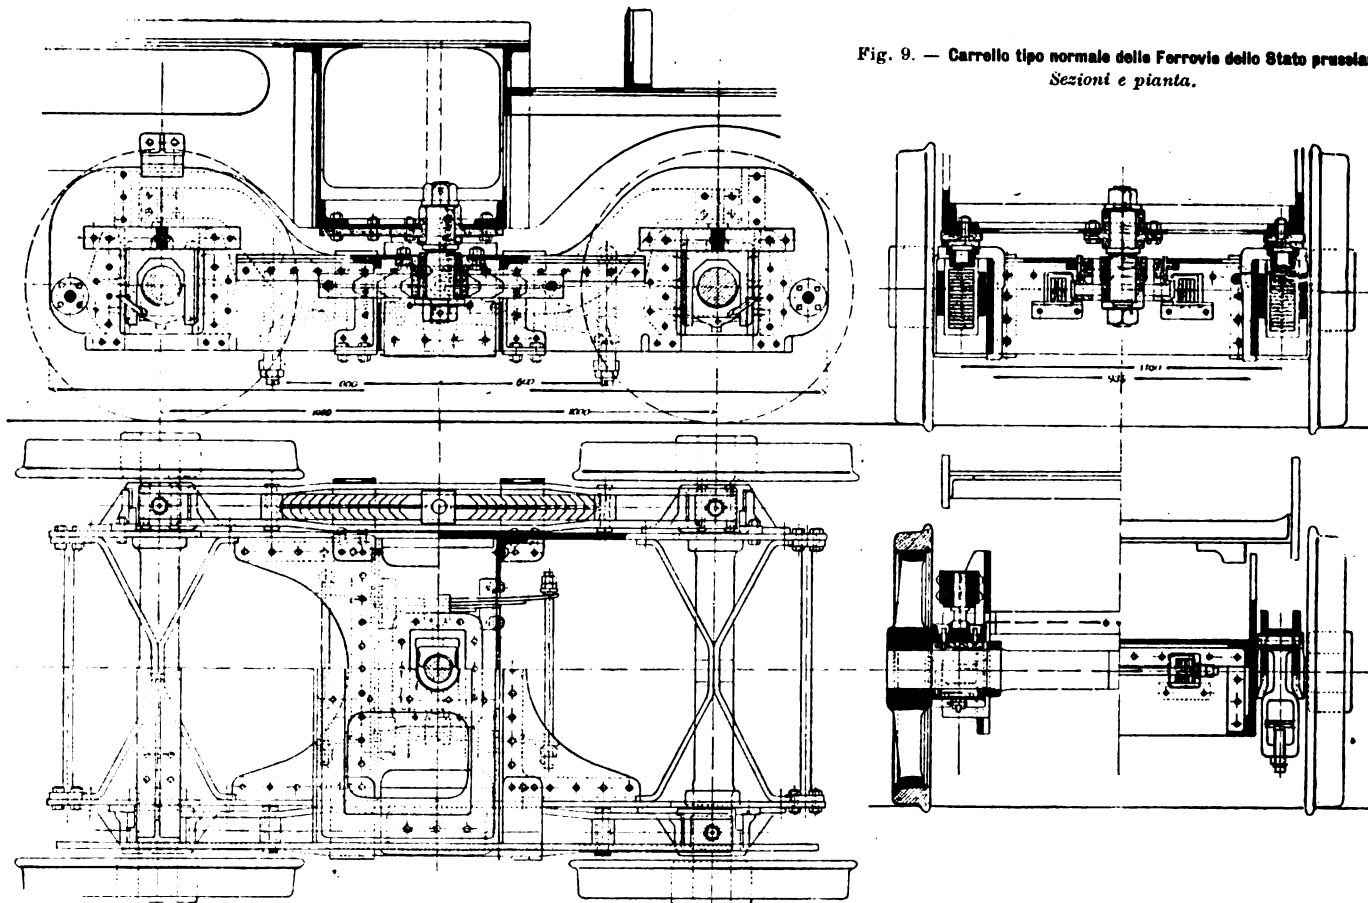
Carrello tipo normale delle Ferrovie dello Stato prussiano. Sezioni e pianta.
